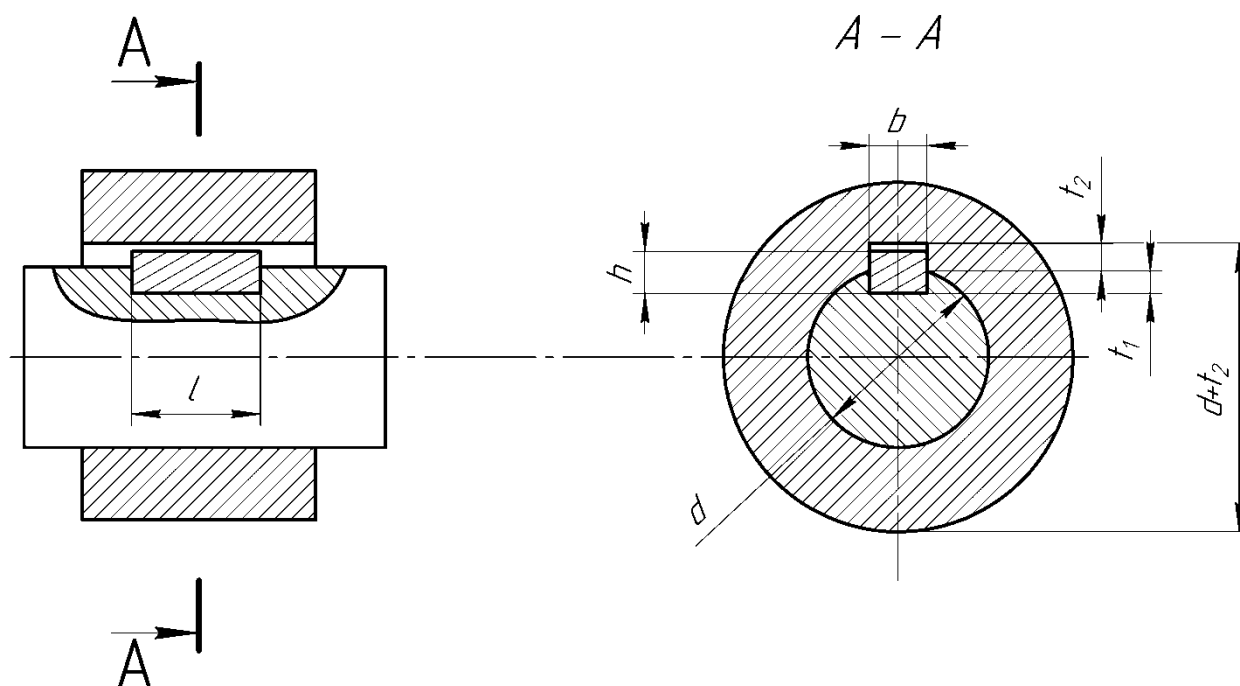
Размеры шпоночного соединения с призматической шпонкой
